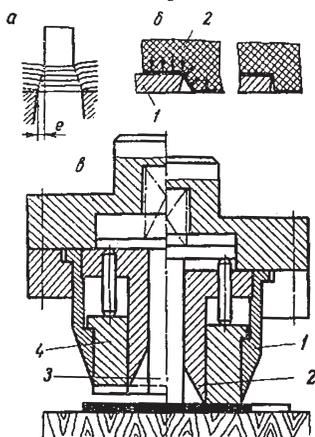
Вырубка и пробивка: 1 – шаблон (пуансон); 2 – листовая резина (матрица); 3, 4 – выталкиватели; а – вырубка-пробивка; б – штамповка резиной; в – вырубка шайбы
